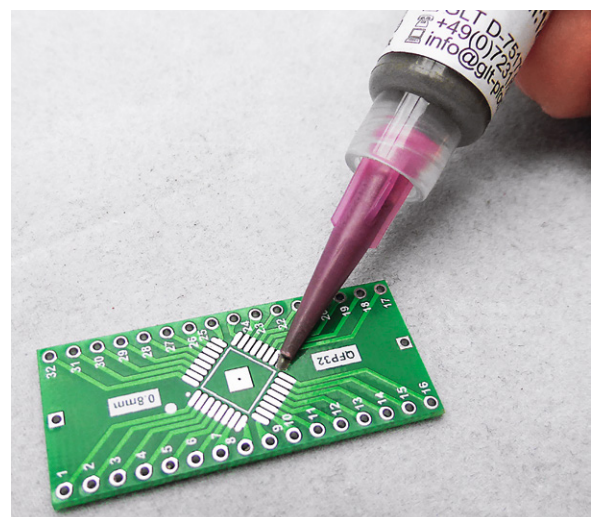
Mit einer Dosierspitze wird das SMD-Lot Pad für Pad aufgetragen.
